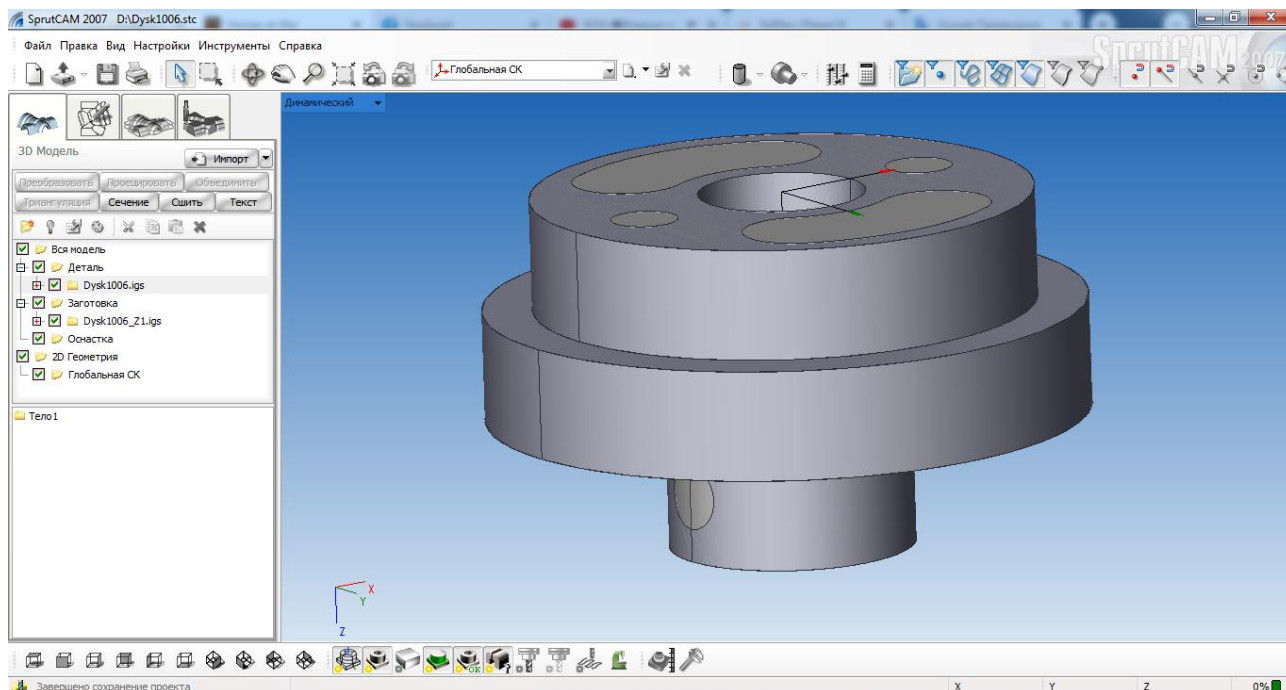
3D-модель заготовки та деталі, імпортовані у систему SprutCAM
